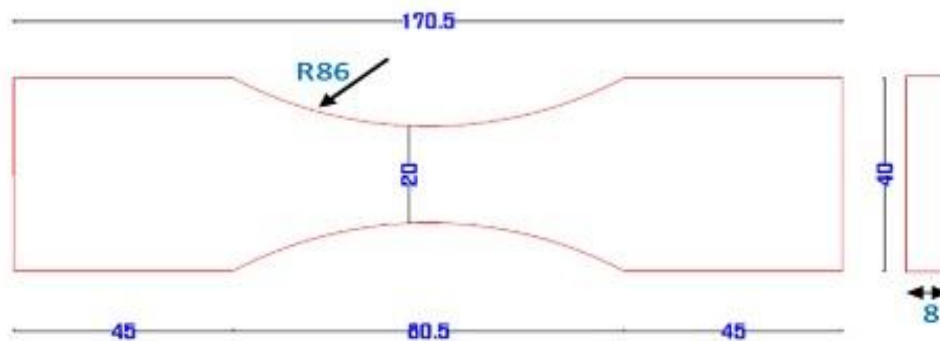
Dimensions de l'éprouvette non soudée
